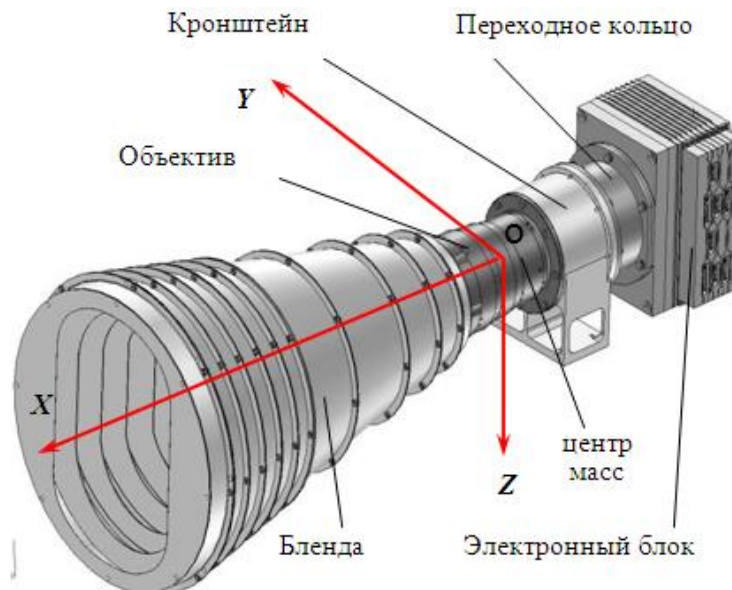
3D-модель звёздного датчика, выполненная в CAD Pro/ENGINEER
